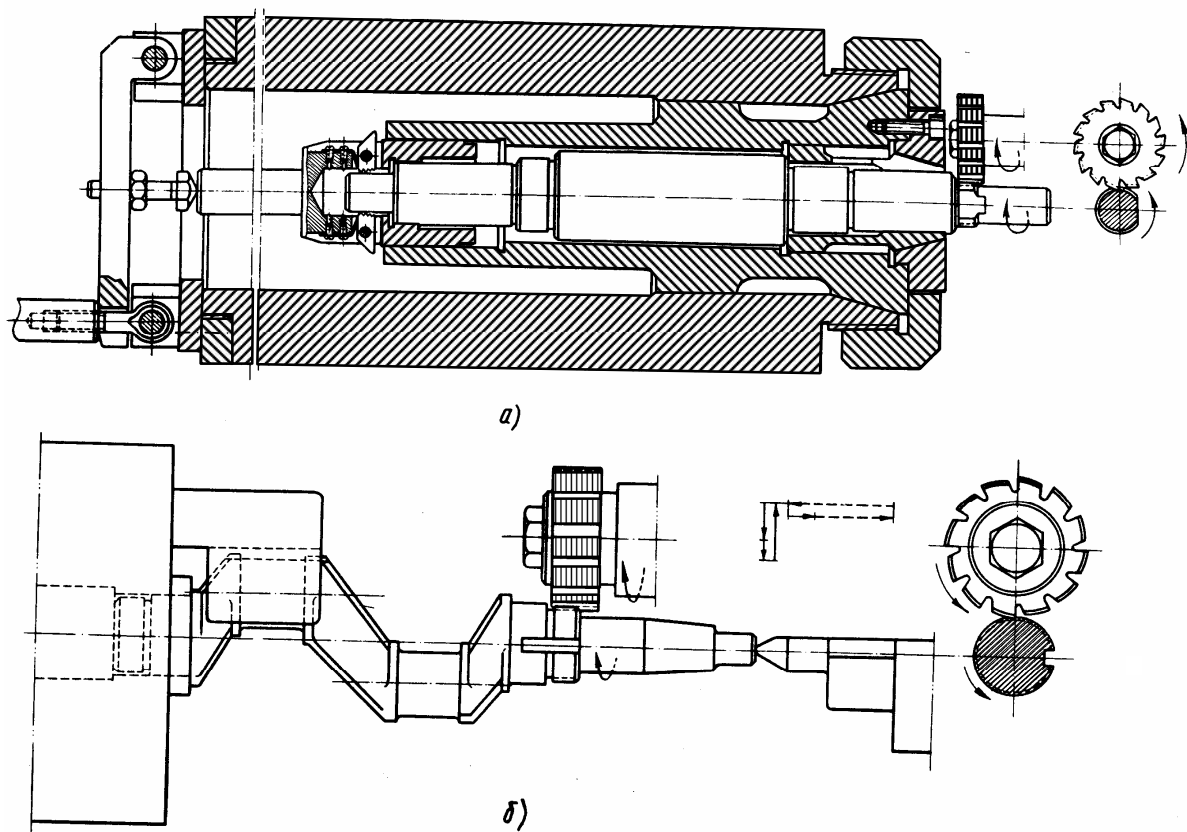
Схеми наладок різьбофрезерного верстата: а – при обробці різьби заготовки, установлені на шпинделі; б – при фрезеруванні різьби на колінчастому валу
